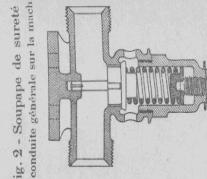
Soucoupe de sûreté de la conduite générale sur la machine
